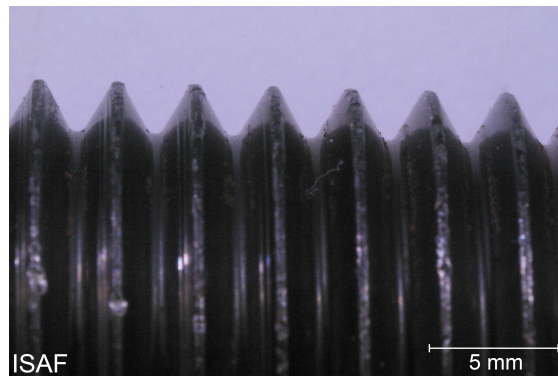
Gewindeprüfkörper axial belastet mit 20kN (Bolzen)
